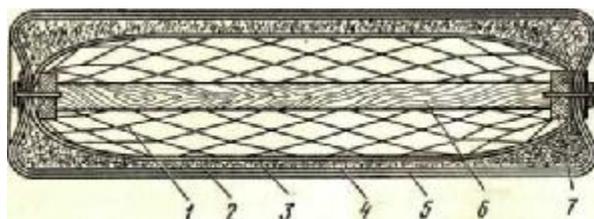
Схема изготовления валика на пружинах непрерывного плетения:
